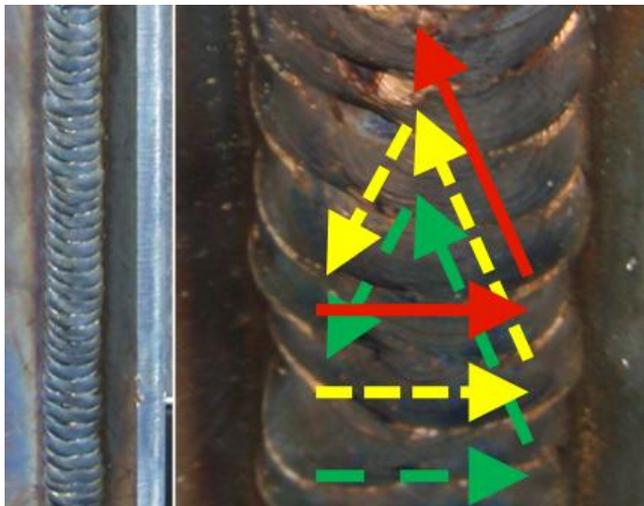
Ein anderer Schweißer mit mehr Energie (Stahl 8mm, M21, 1mm G3Si1)
